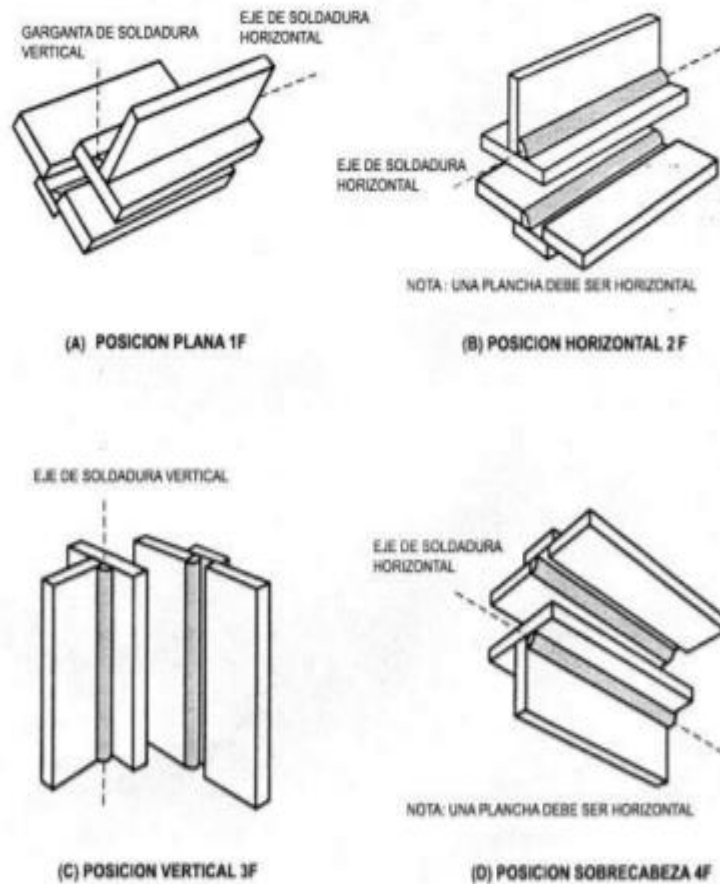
Posiciones de Plancha de Ensayo para Soldaduras de Filete (ver 4.2.4)
